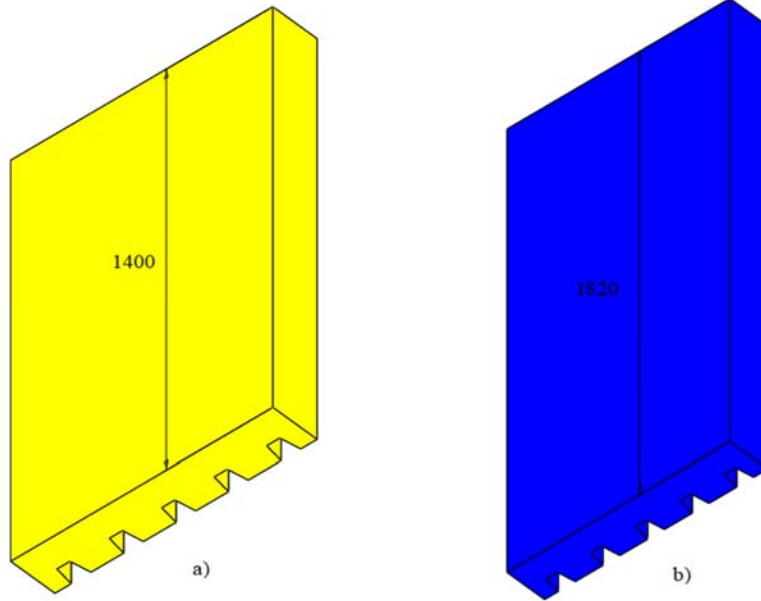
Trapez kollektör hava giriş kesiti görünümü (Trapezoidal collector air inlet section view)
